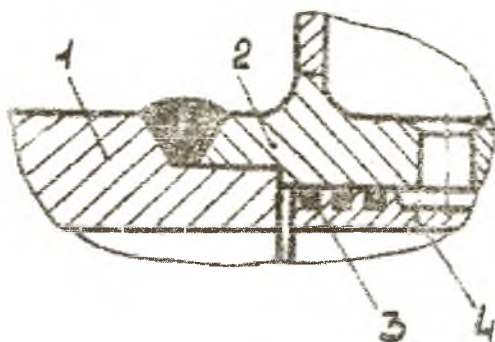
Соединение головки с корпусом камеры при установке коллектора для вывода охладителя: 1 – корпус головки; 2 – корпус коллектора; 3 – припой; 4 – стенка корпуса камеры
